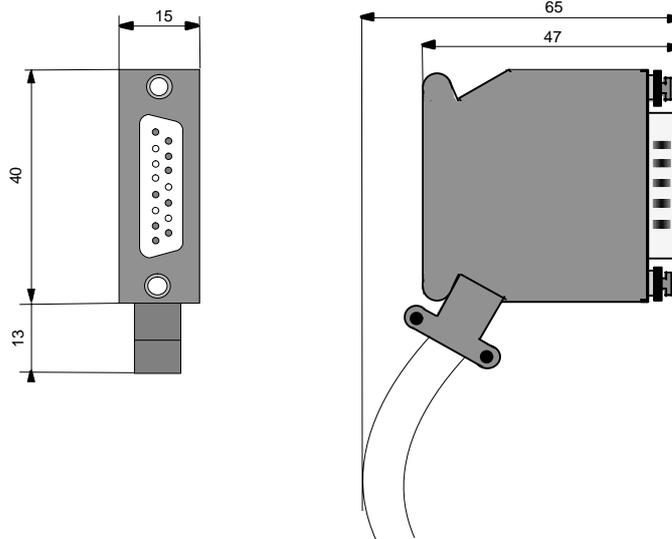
15-poliger Sub-D-Stecker für Selbstmontage (Maße in mm)
